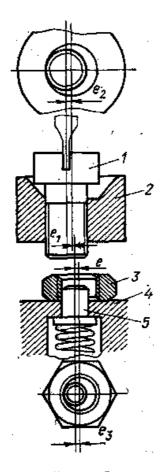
Несовпадение осей при сборке двух резьбовых деталей
